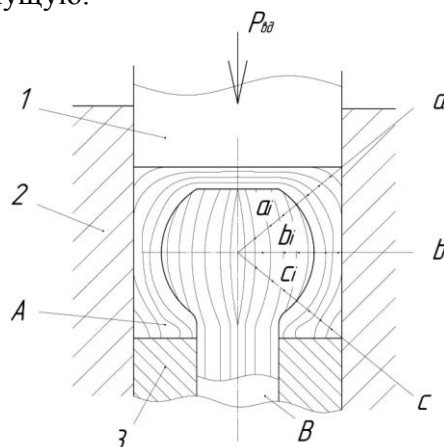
Схема формообразования составного стержневого изделия из сборной заготовки (А – головная заготовка; В – стержневая заготовка):
